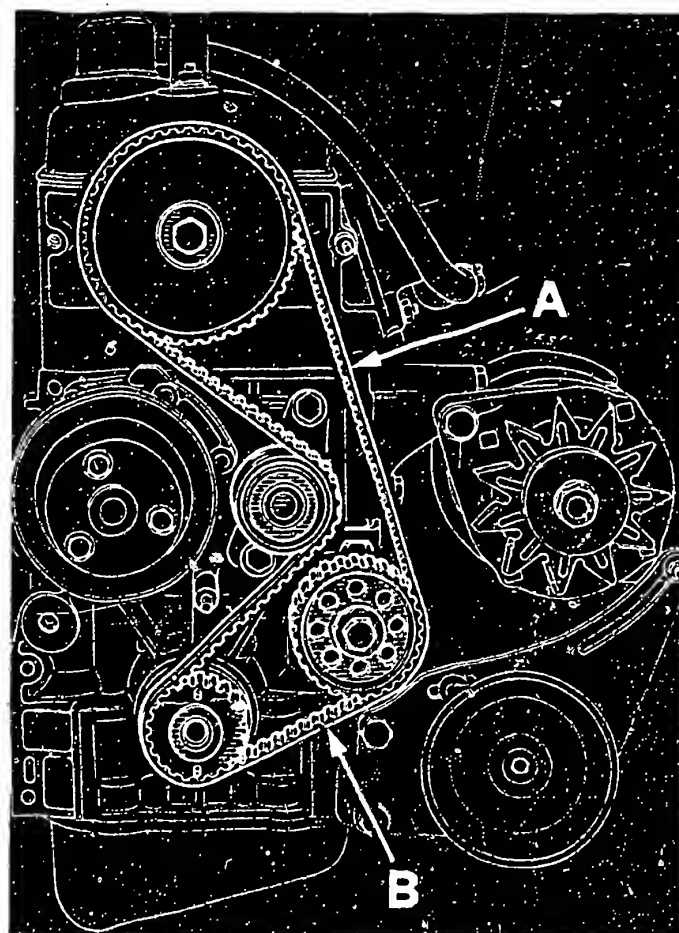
Auflegen des Zahnriemens beim Motor J7T: Die Seiten A und B sind gespannt.
